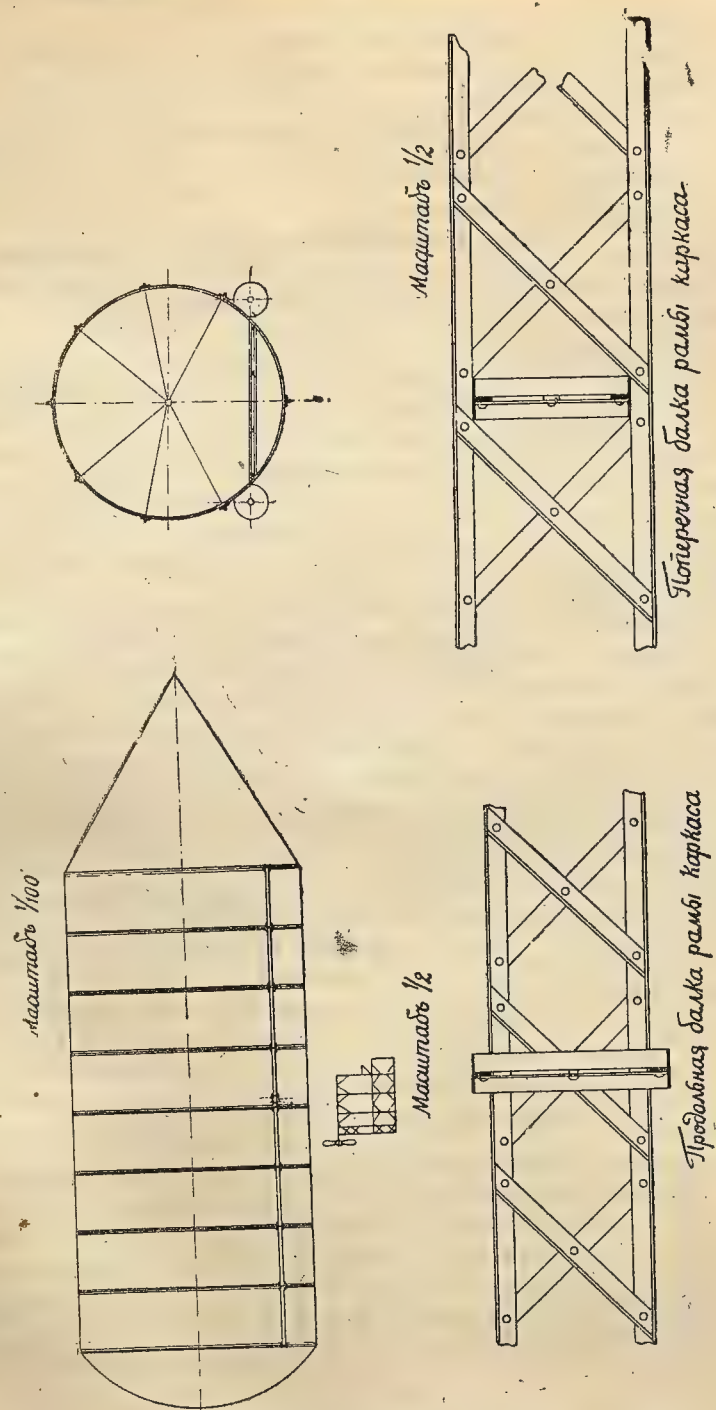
Схематический чертеж аэростата Шварца (ЦГВИАЛ)
